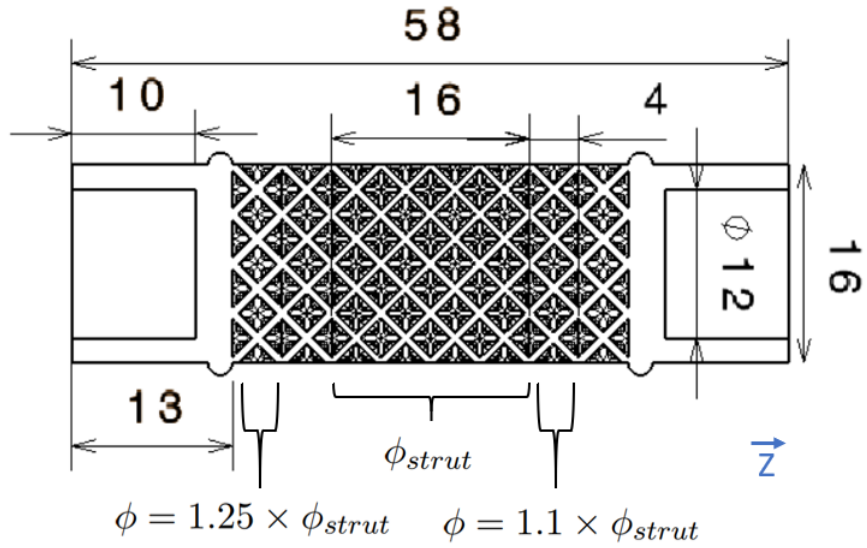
Dimensions des éprouvettes en mm. Direction de fabrication : (\vec{Z}).
